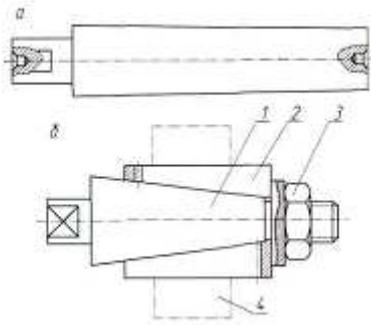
Оправки для установки заготовок типа «втулка»: а – длинные центровые с конусностью  $< 0,015$  мм на 100 мм длины; б – разжимные: 1 – наружный конус; 2 – разжимная втулка; 3 – гайка
